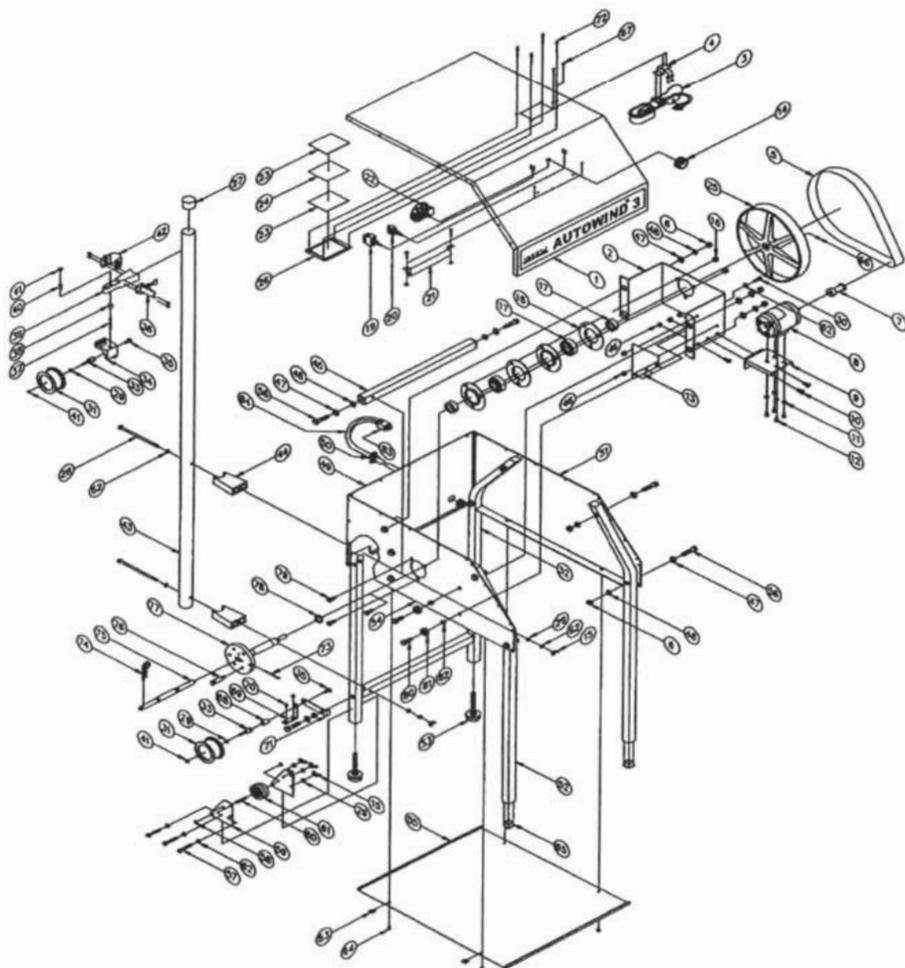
Diagrama de Ensamble de la Mesa de Armado
